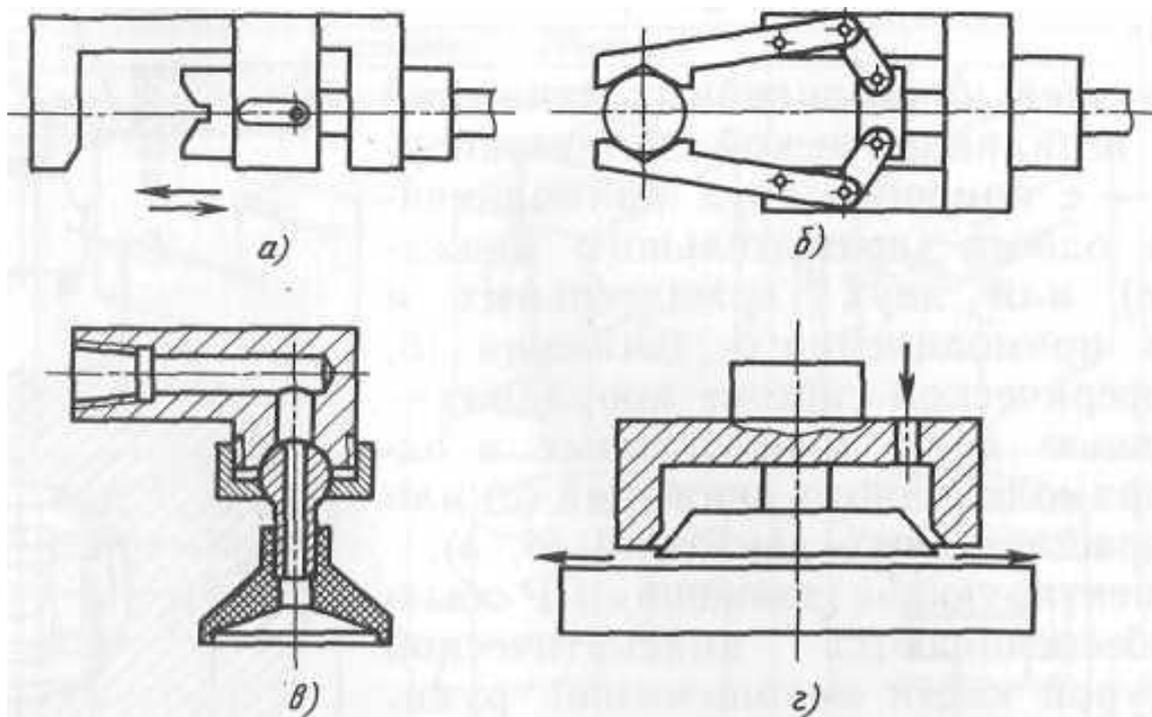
Типы хватных устройств: а – с одной подвижной губкой; б – с двумя подвижными губками; в – вакуумный; г – струйный
